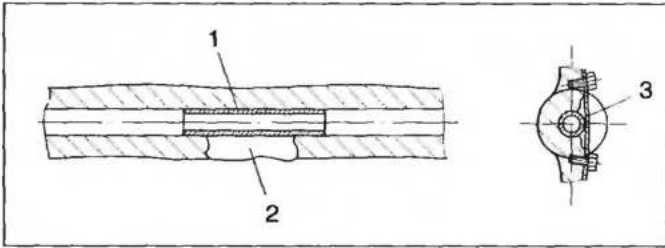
Установка трубки в поврежденный масляный канал блока цилиндров: 1 — трубка; 2 — пробоина в стенке; 3 — накладка для прижима трубки
